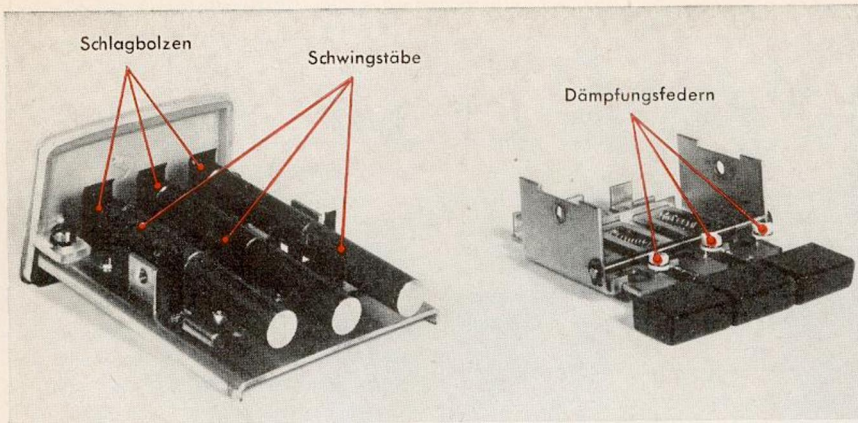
Der einfache mechanische Aufbau mit den drei Schwingstäben zeigt sich besonders deutlich, wenn die Tastenhalterung gelöst wird.
